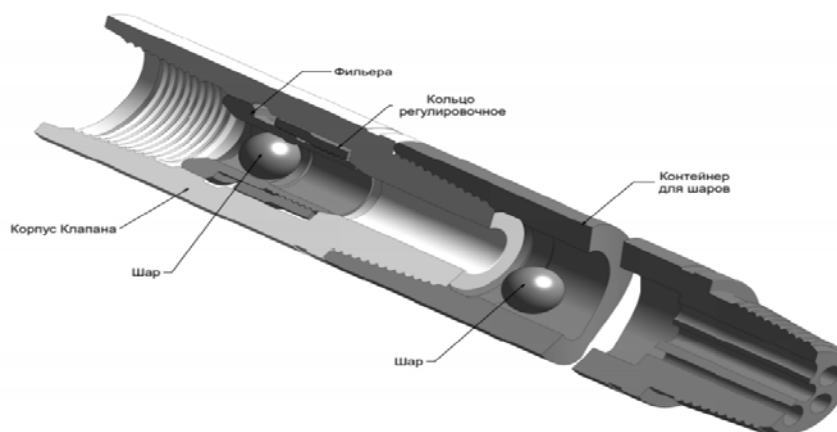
Вид устройства клапана опрессовочного многократного действия в разрезе
